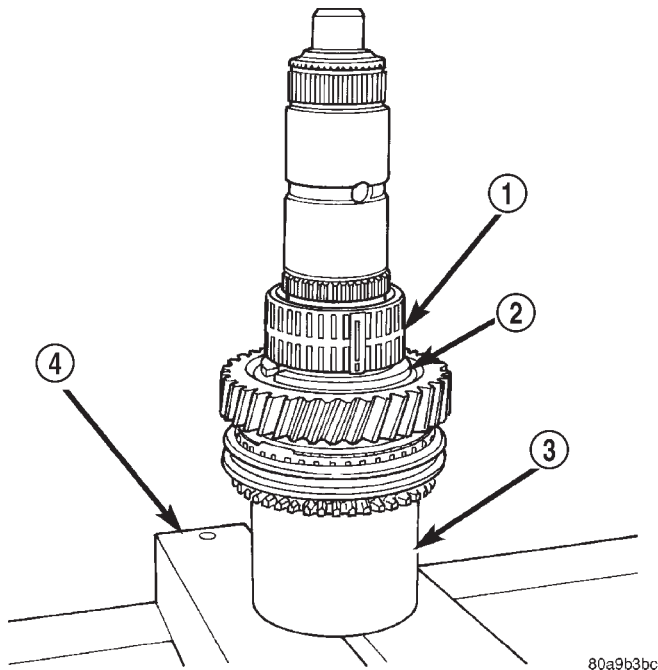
COJINETE DEL ENGRANAJE DE PRIMERA
